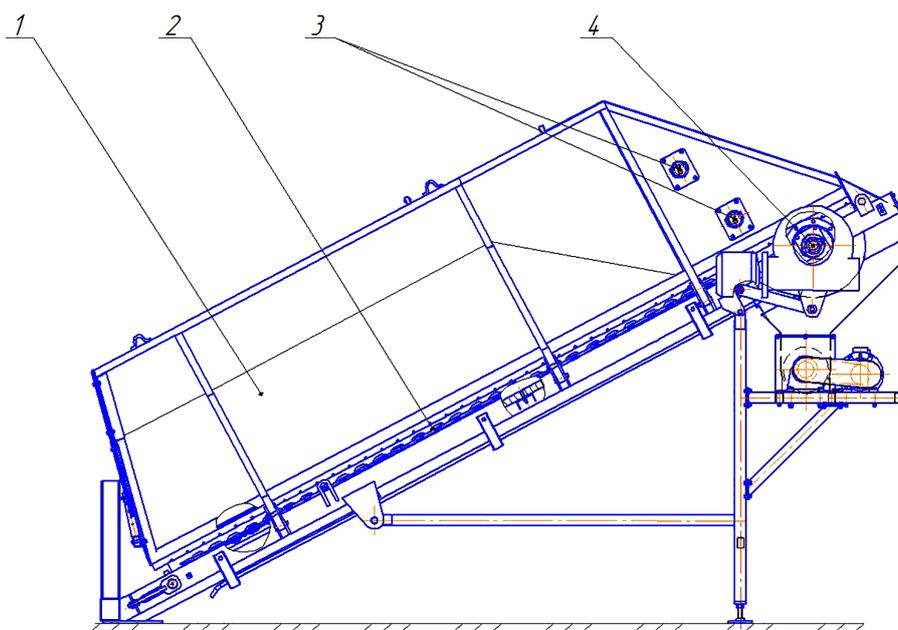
Общий вид питателя-измельчителя кормов: 1 – бункер; 2 – подающий транспортер; 3 – блок битеров; 4 –измельчитель
